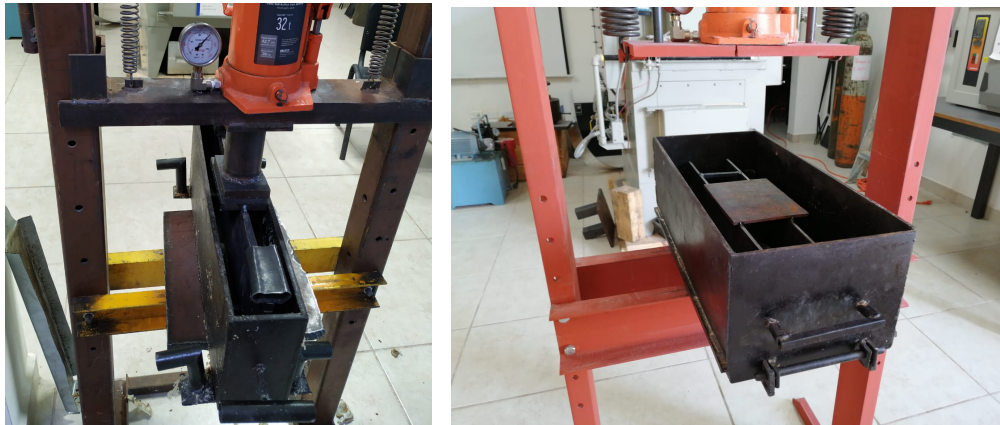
Moldes para conformación de barrote y panel. a) Izquierda molde para barrote, b) derecha molde para panel.
